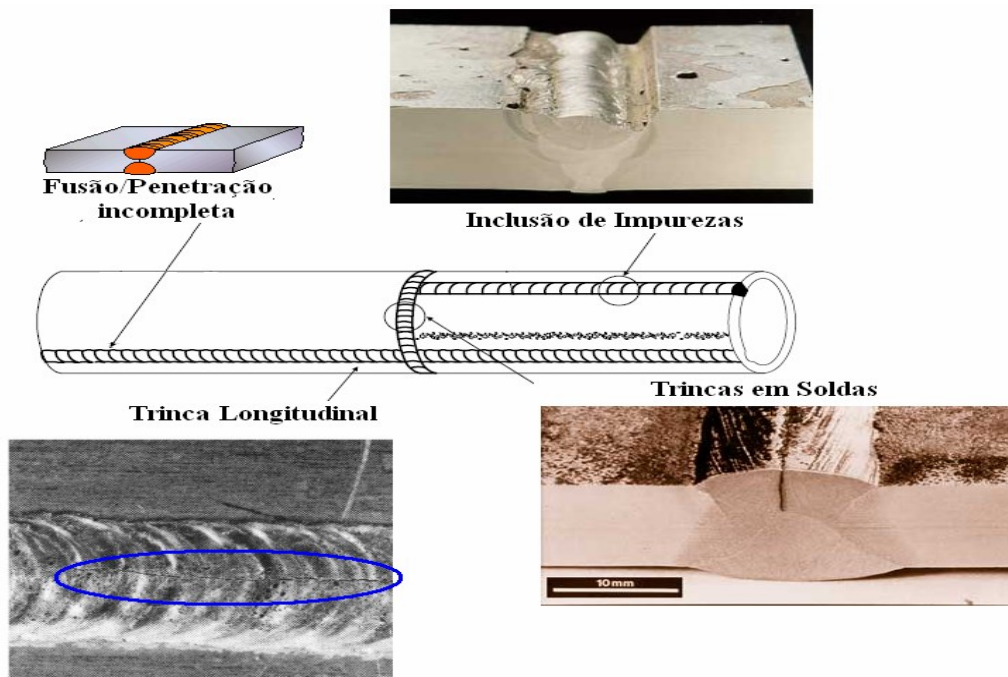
Exemplos de defeitos de soldagem (CABRAL).
